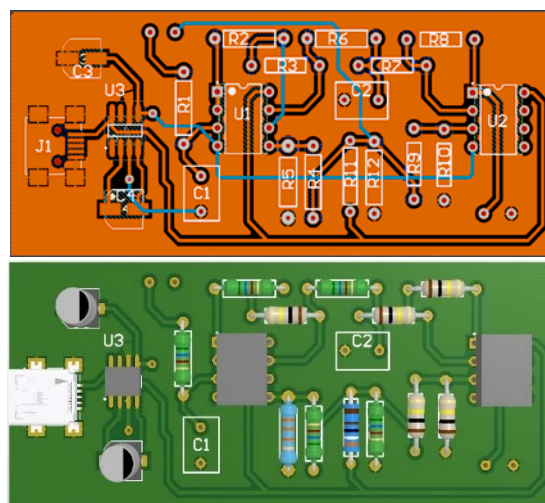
PCB del sistema acondicionador en Circuit Maker.
